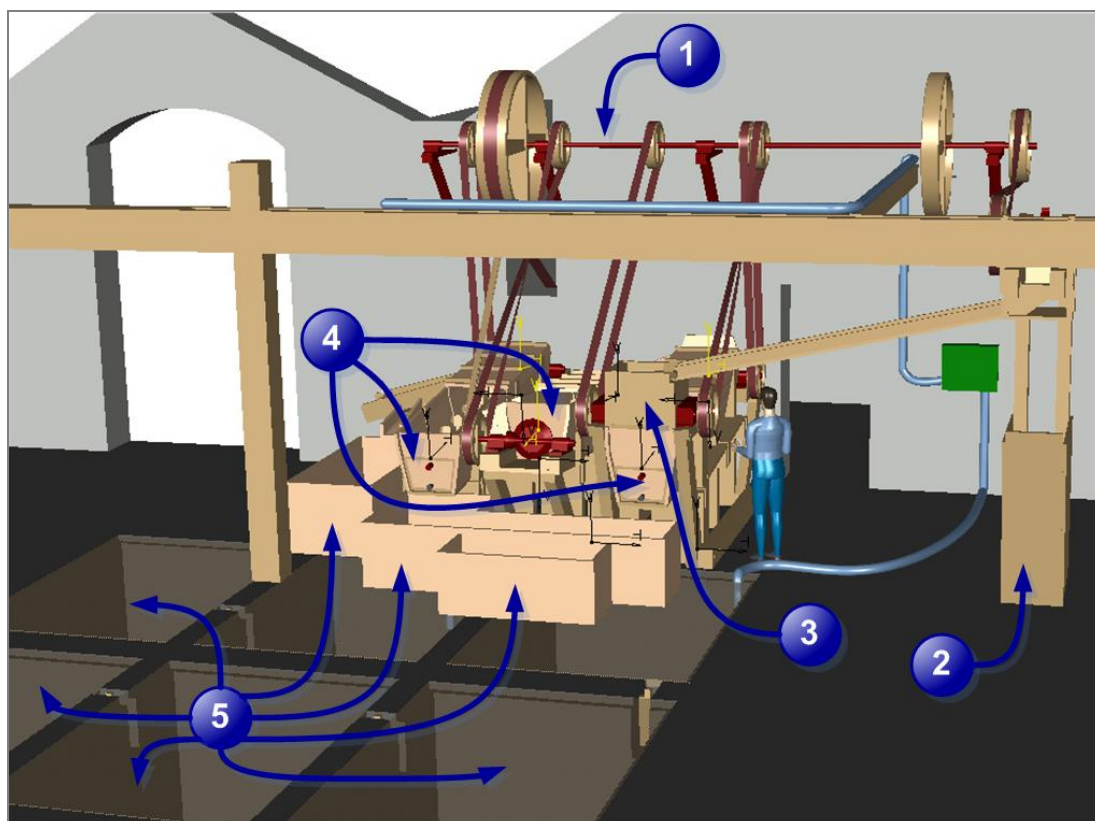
MAQUETTE NUMERIQUE, VUE D'ENSEMBLE DE LA MACHINE
